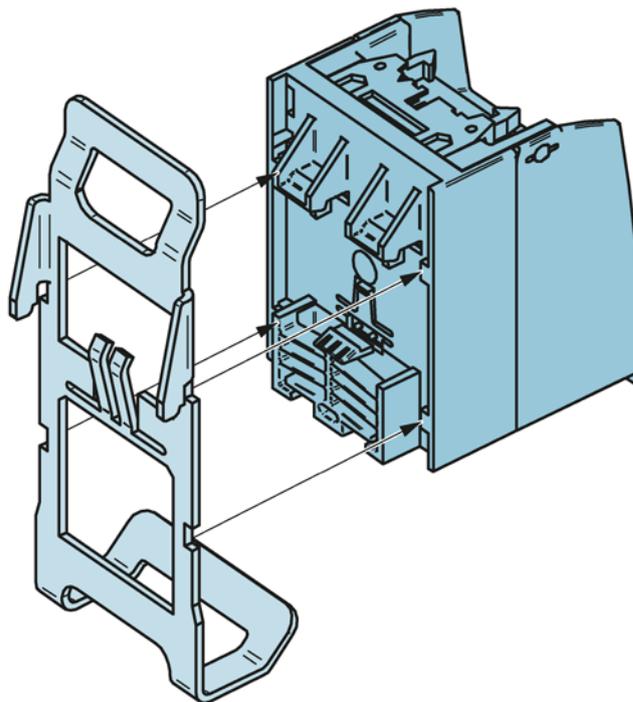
Aussparungen des Schirmblechs in Gegenform einpassen (Beispielgrafik)
